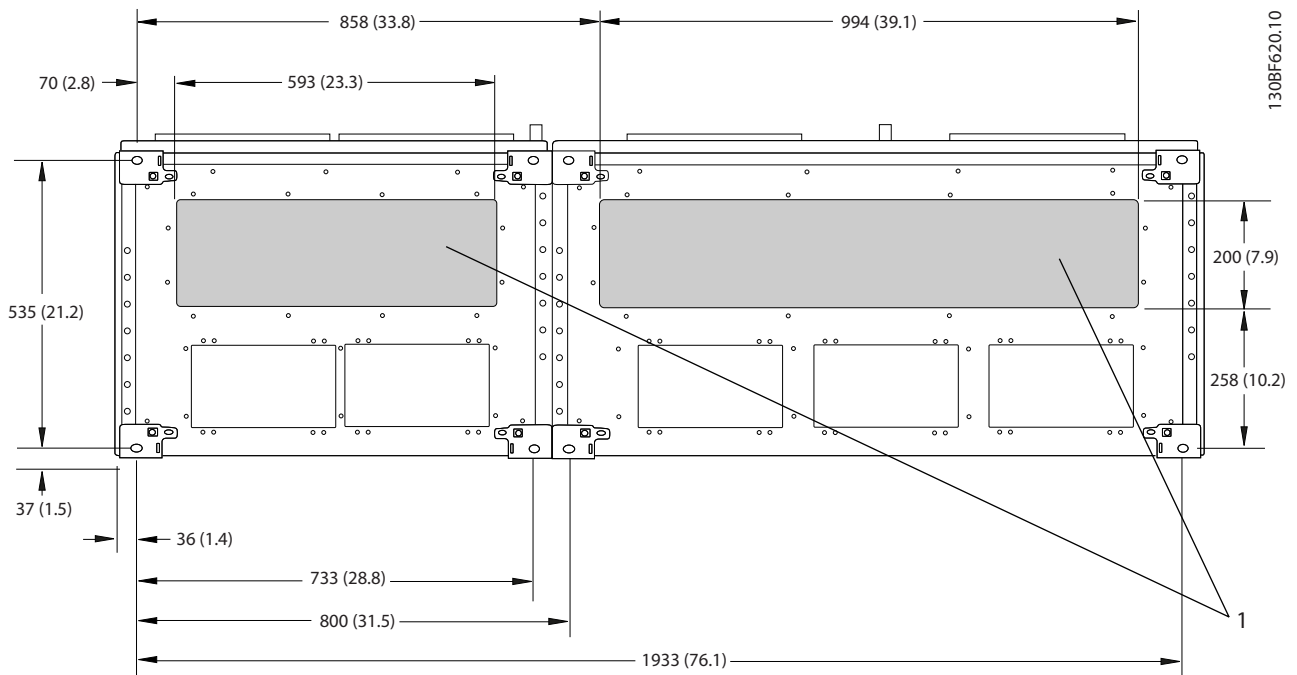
Klemafmetingen voor omvormerkast F10-F11, zijaanzicht
